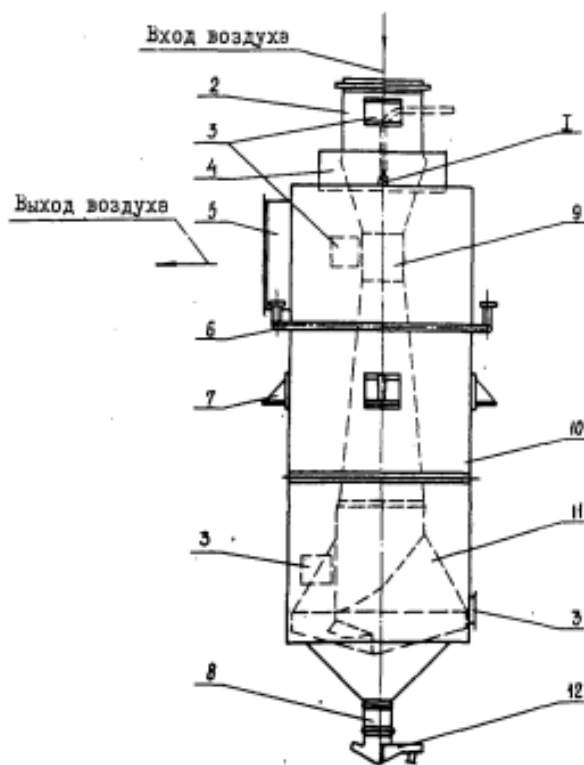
Пылеуловитель КЦМП: 1 — сопло центральное; 2 — патрубок входной; 3 — люк; 4 — водяная камера; 5 — отводной патрубок; 6 — коллектор; 7 — лапа опорная; 8 — сливной патрубок; 9 — труба-коагулятор; 10 — каплеуловитель; 11 — закручиватель; 12 — гидрозатвор
